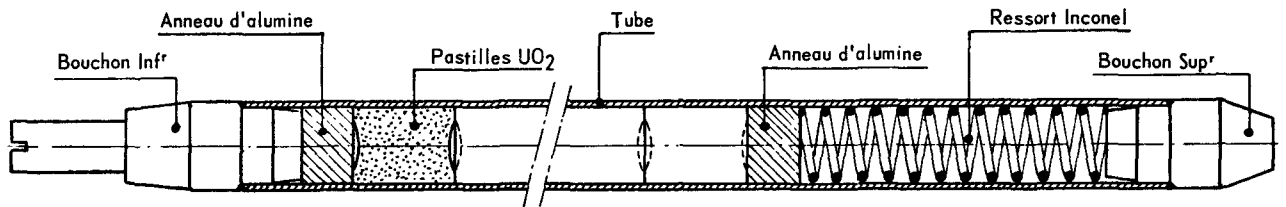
BR3. Élément expérimental. Vue d'ensemble
